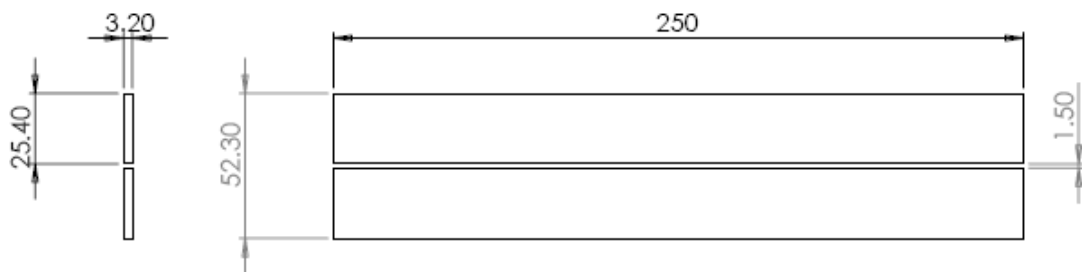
Dimensões e geometria da junta utilizada para soldagens com transferência por curto-circuito
